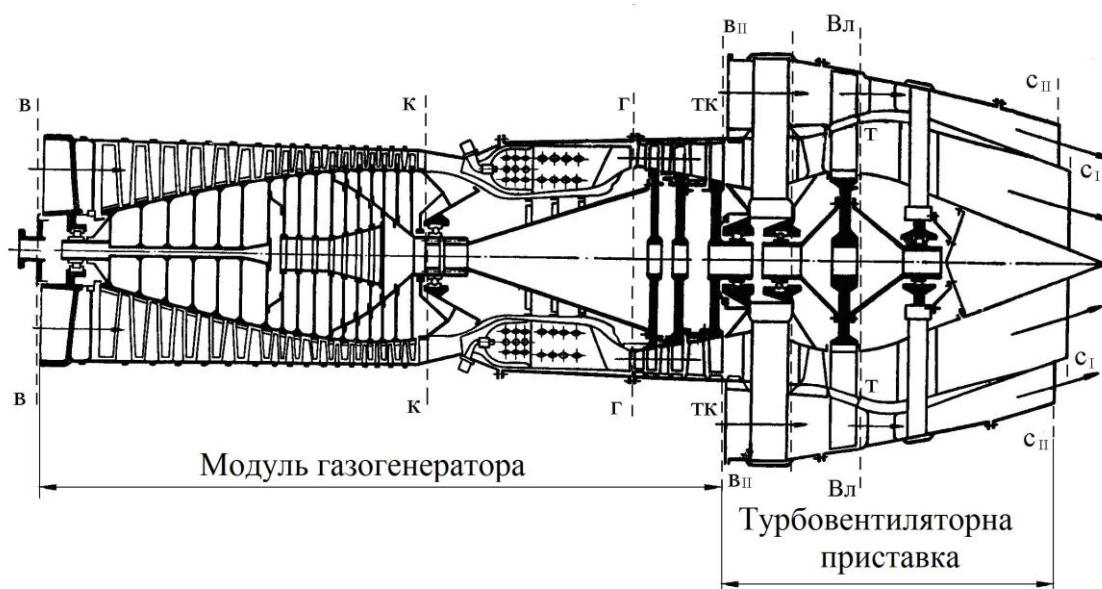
Схема ТРДД на базі модуля газогенератора ТРД J -79
